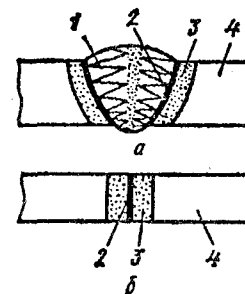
Схема сварного соединения (а — при сварке плавлением; б — при сварке давлением): 1 — сварной шов; 2 — зона сплавления; 3 — зона термического влияния; 4 — основной металл
